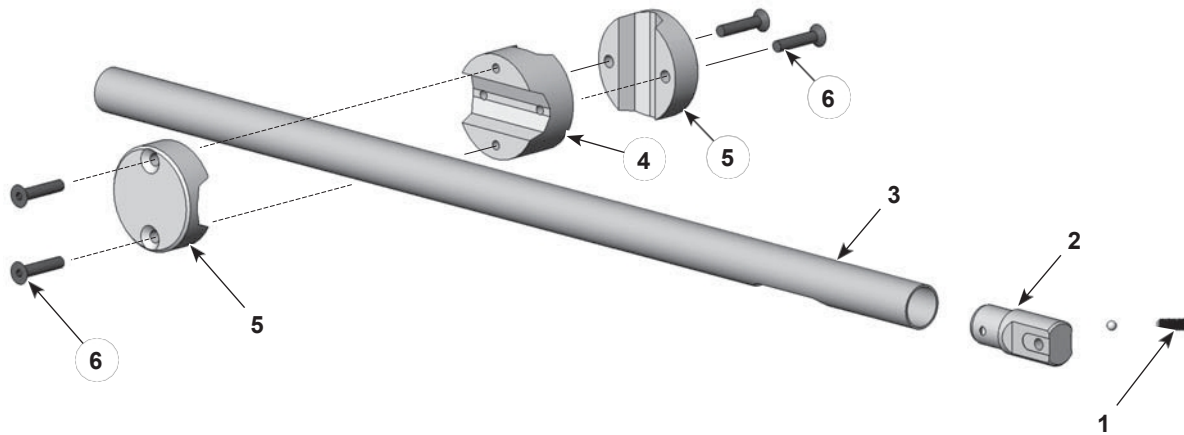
Opcjonalny przegubowy pręt pistoletu
